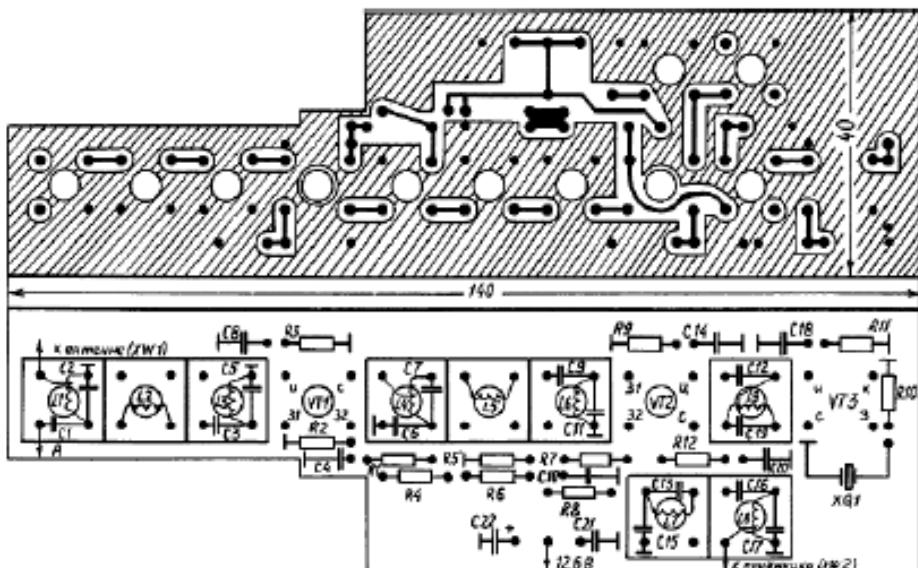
Эскизы монтажной платы конвертера и расположения деталей на ней
